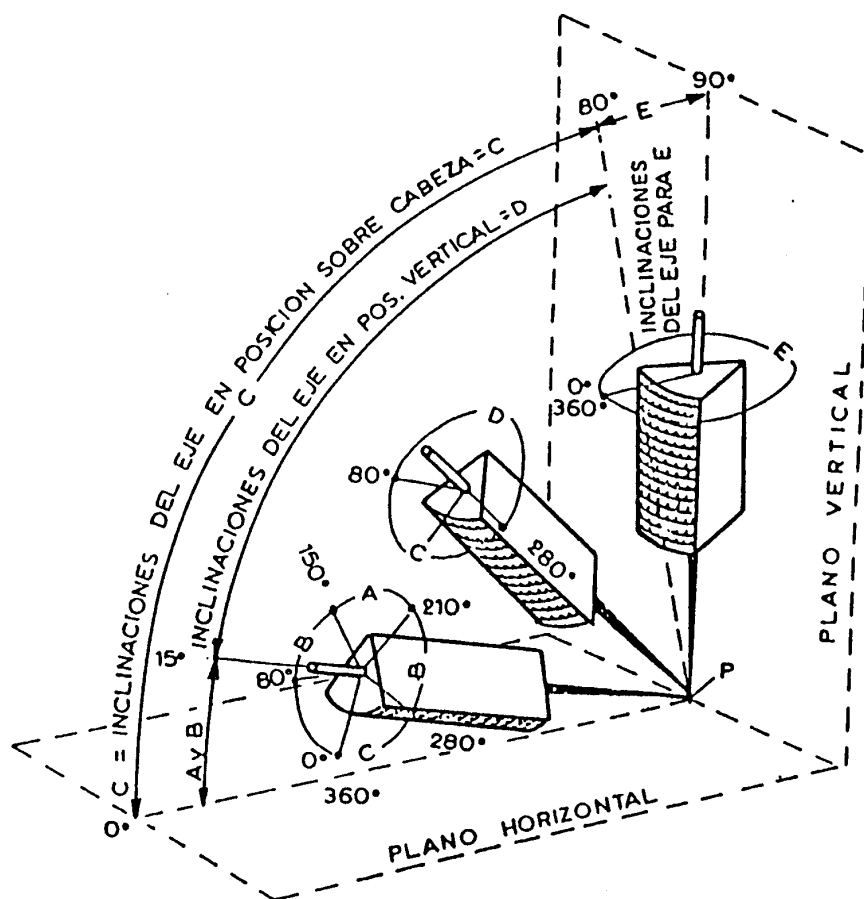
(Artículo 7° inciso 4, letras a) y b). Posiciones límites de la inclinación del eje y de la rotación de la cara de la soldadura en las distintas posiciones de soldar a tope planchas y cañerías
